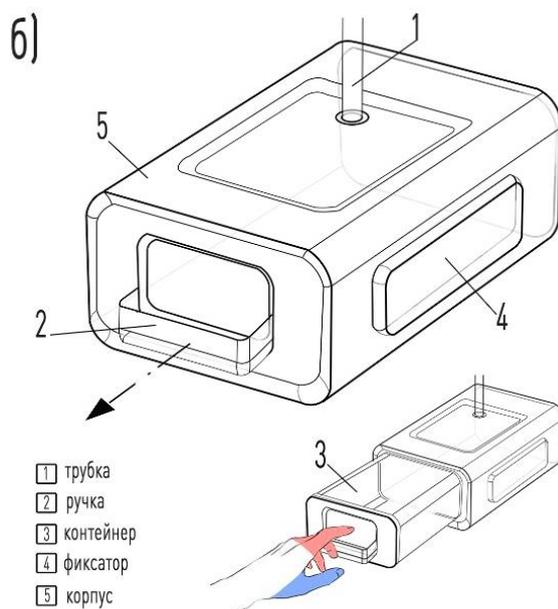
Корпус маслосборника: 1 – трубка; 2 – ручка; 3 – лоток; 4 – фиксатор
